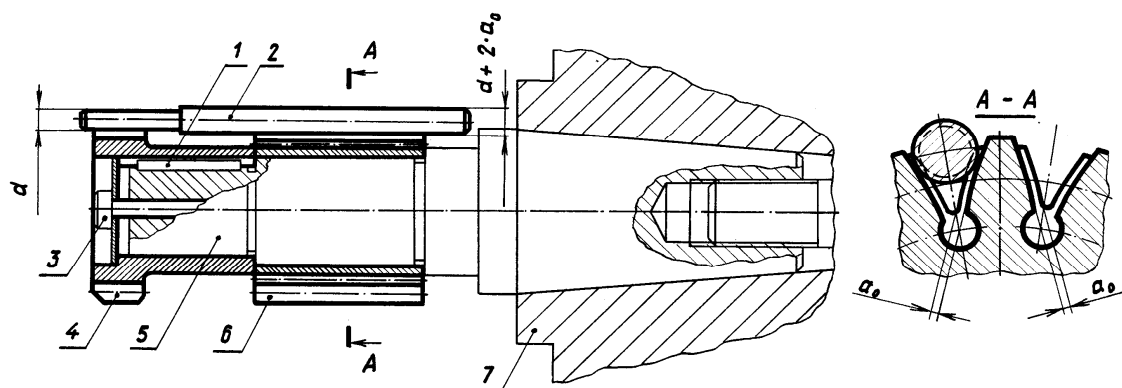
Схема установки обкаточного катода. 1-шпонка; 2 - ступенчатый ролик; 3-винт; 4-эталонная шестерня; 5-оправка; 6-обкаточный катод; 7-шпиндель инструментальной головки.
